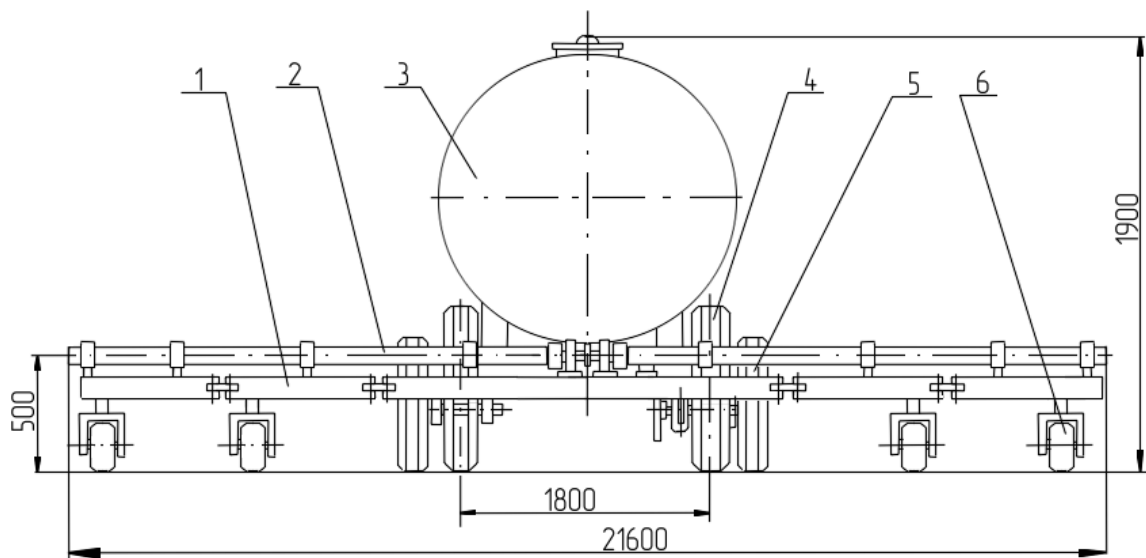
Общий вид агрегата для внесения ЖКУ шириной захвата 21,6 м (вид сзади): 1 – рама; 2 – полиэтиленовый кожух; 3 – ёмкость; 4 – опорное колесо; 5 – приводное колесо; 6 – самоустанавливающиеся колеса
